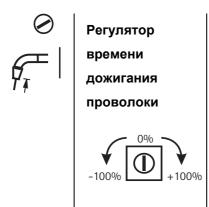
/3. Органы настройки, расположенные в сварочном аппарате
